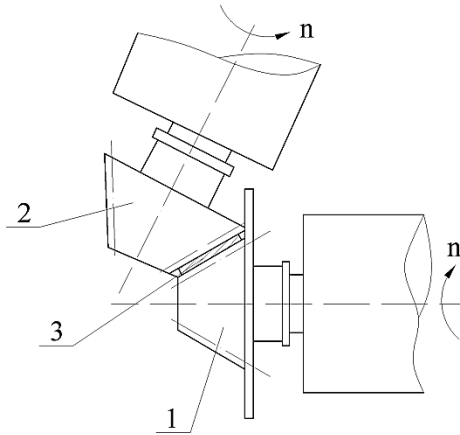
Схема утворення гофрованої поверхні конічними колесами:
